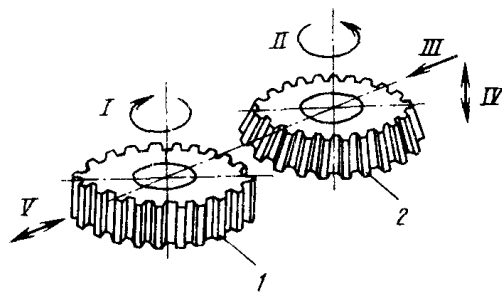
Схема зубодолбления цилиндрических зубчатых колес: I – движение заготовки зубчатого колеса; II – движение долбяка; III – движение подачи врезания; IV – возвратно-поступательное движение долбяка; V – движение отвода заготовки; 1 – заготовка, 2 – долбяк
